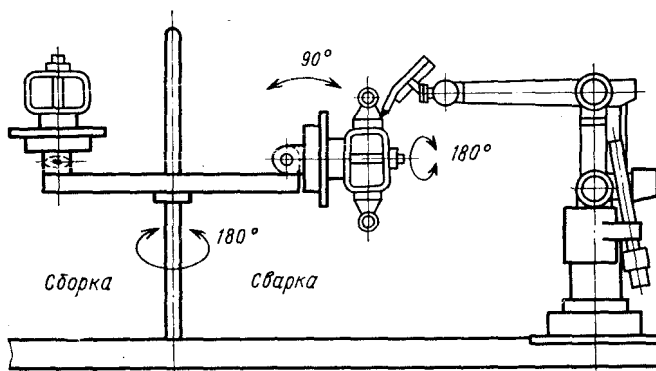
Схема РТК для сборки и сварки поперечины рамы грузового автомобиля
